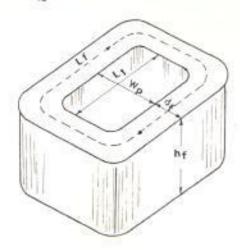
DIMENSIONES DE LA BOBINA DE CAMPO
